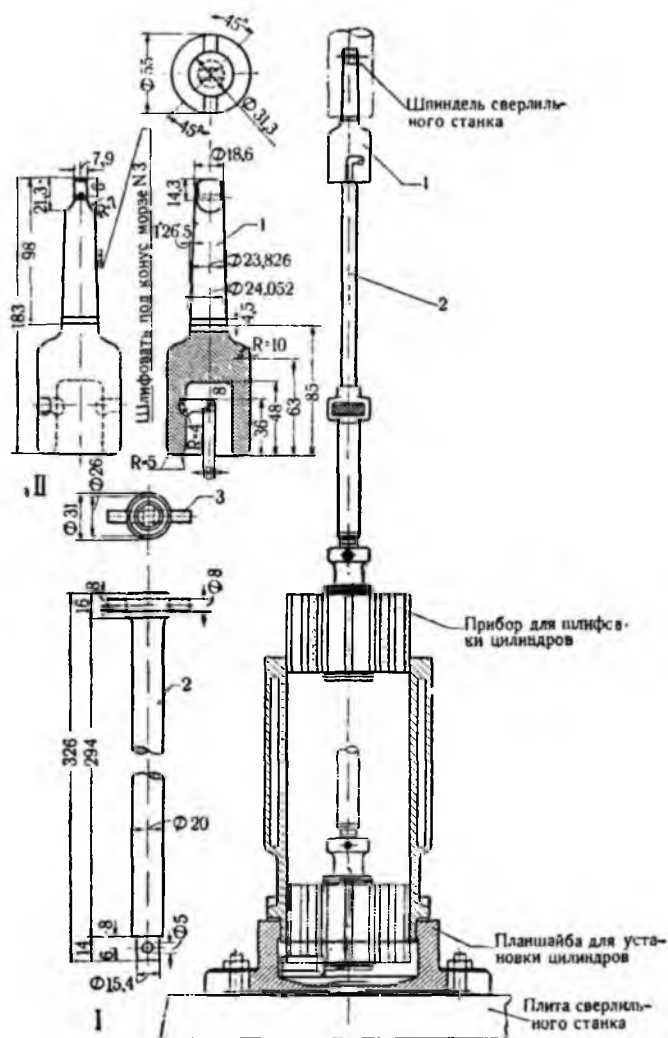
Шлифовка цилиндров ЧТЗ-С-60 прибором с двойным шарниром:
